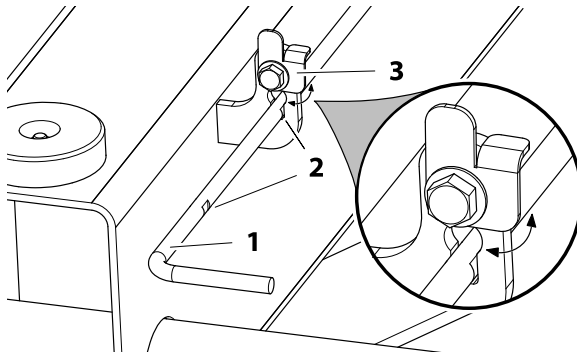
Nůžková konstrukce – sestava bezpečnostní podpěry
